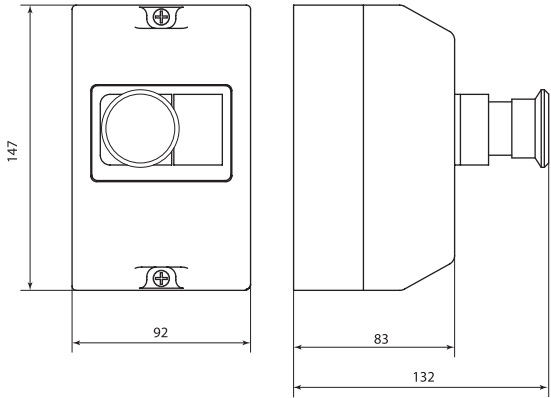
Габаритные и установочные размеры защитной оболочки
